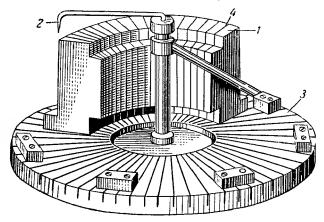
Сборка пластин коллектора на диске: 1 — пластины мелные; 2 — рейсмус; 3 — сборный диск; 4 — миканитовые пластины.
